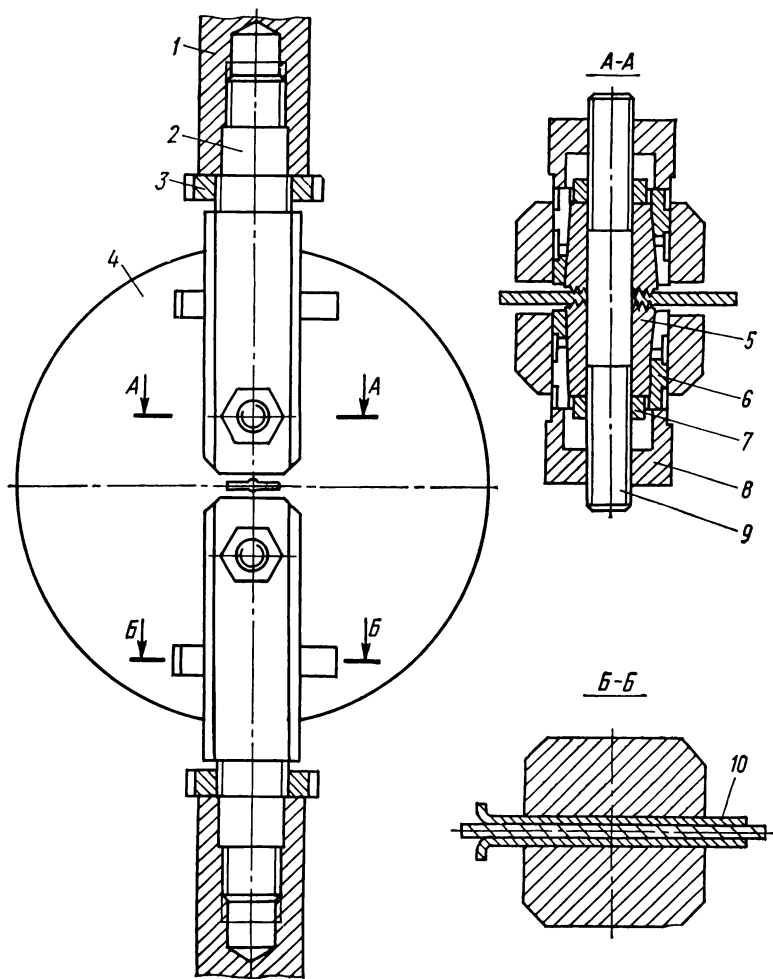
Приспособление для крепления образцов  $D_2$ —В—Р и  $K_2$ —В—Р:
